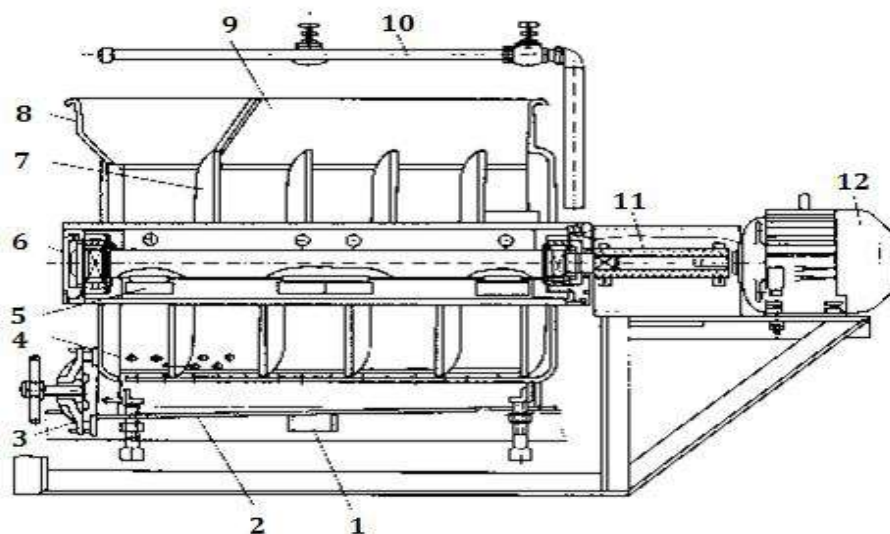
Машина вібраційна мийна ММКВ-2000: 1 - зливний патрубок; 2 - лоток; 3 - заглушка; 4 - отвори; 5 - дисбаланси; 6 - вал; 7 - шнек; 8 - завантажувальний пристрій; 9 - короб; 10- водопровід; 11- гнучка муфта; 12 – електродвигун.
